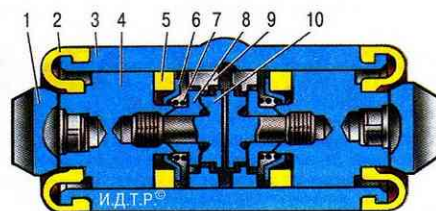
Колесный цилиндр: 1 - упор колодки; 2 - защитный колпачок; 3 - корпус цилиндра; 4 - поршень; 5 - уплотнитель; 6 - опорная тарелка; 7 - пружина; 8 - сухари; 9 - упорное кольцо; 10 - упорный винт; 11 - штуцер; А - прорезь на упорном кольце
